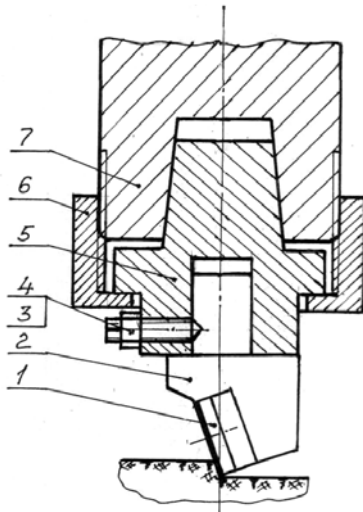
Загальний вигляд алмазно-твердосплавної пластини (АТП)
